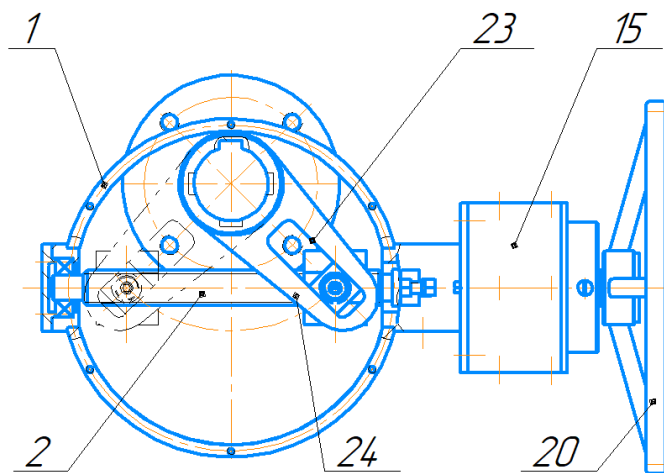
Привод ручной двухскоростной неполноповоротный. Вид сверху
